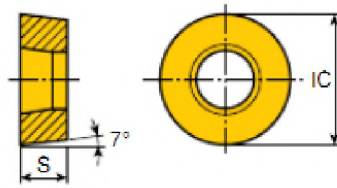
Пластина RCMX 160600 CVD покриття : TT8125B
